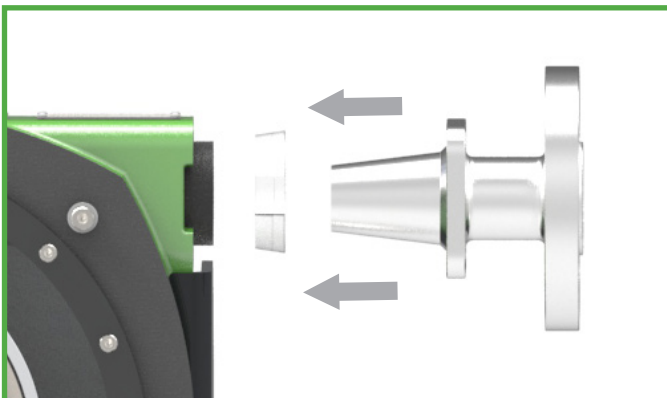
Einführung des Einsatzes für den Anschlussflansch
